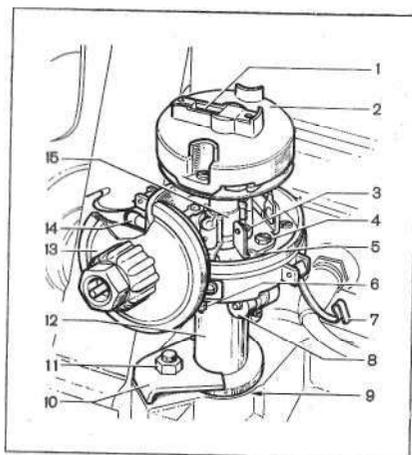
Распределитель зажигания: 1 — помещающее сопротивление; 2 — бегунок ротора; 3 — контакты прерывателя; 4 — винт; 5 — паз; 6 — клемма; 7 — пружинная защелка; 8 — конденсатор; 9 — октан-корректор; 10 — кронштейн; 11 — гайка; 12 — корпус; 13 — вакуумный корректор; 14 — масленка; 15 — кулачок
